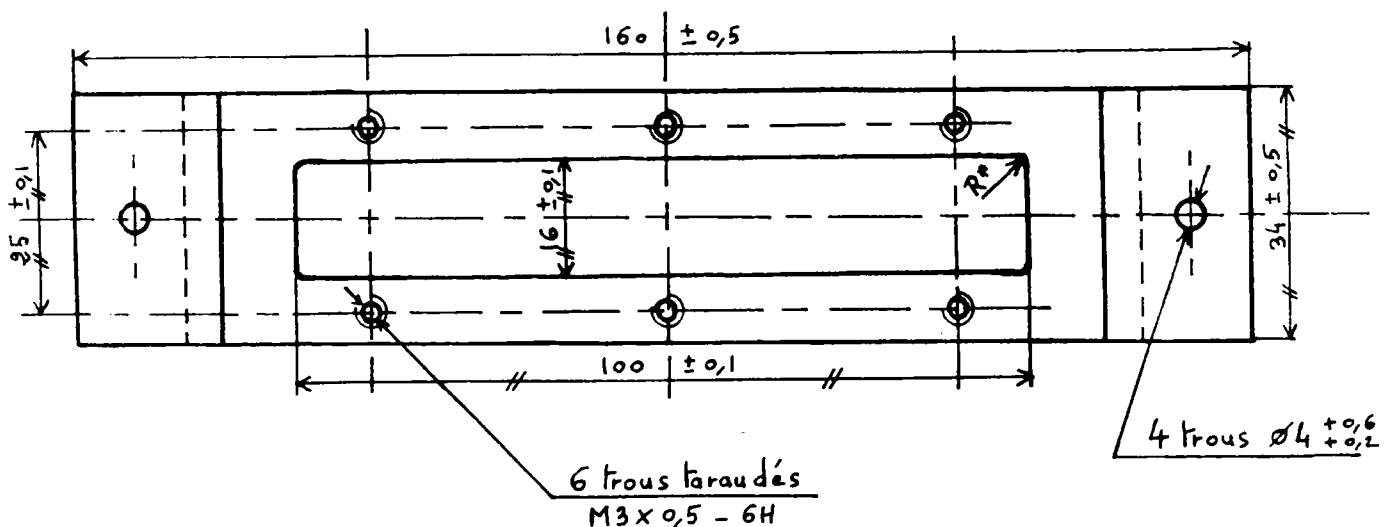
Moule servant à la fabrication des éprouvettes de flexion.
